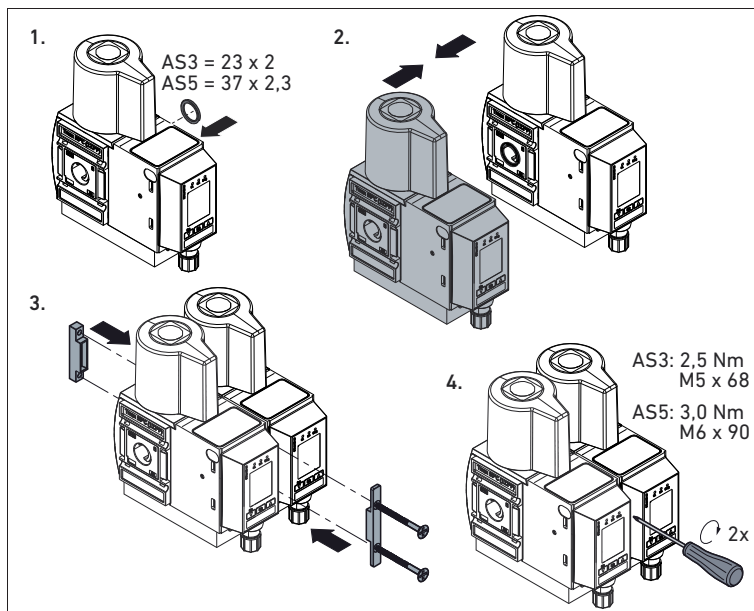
Fijación del elemento de conexión en válvulas bloqueadas
